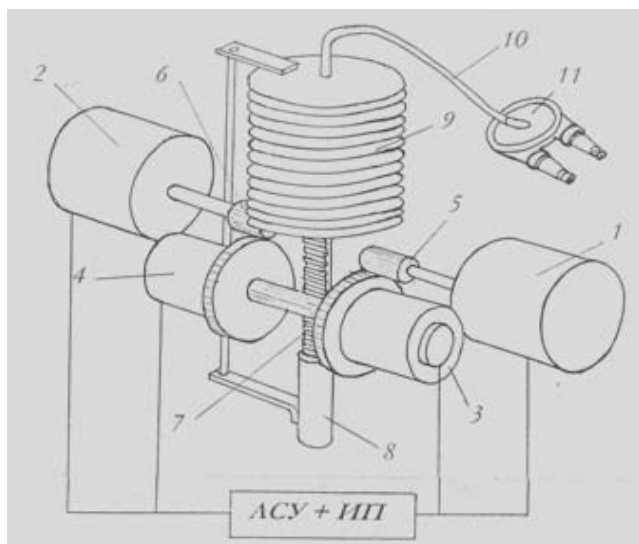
Устройство СЭ ОЛЖ на базе ЭМП речного типа: 1,2 – электродвигатель; 3,4 – электромуфта; 5,6 – зубчатая передача; 7 – рейка; 8 – направляющая рейки; 9 – сильфон; 10 – ПФ; 11 – НВК
